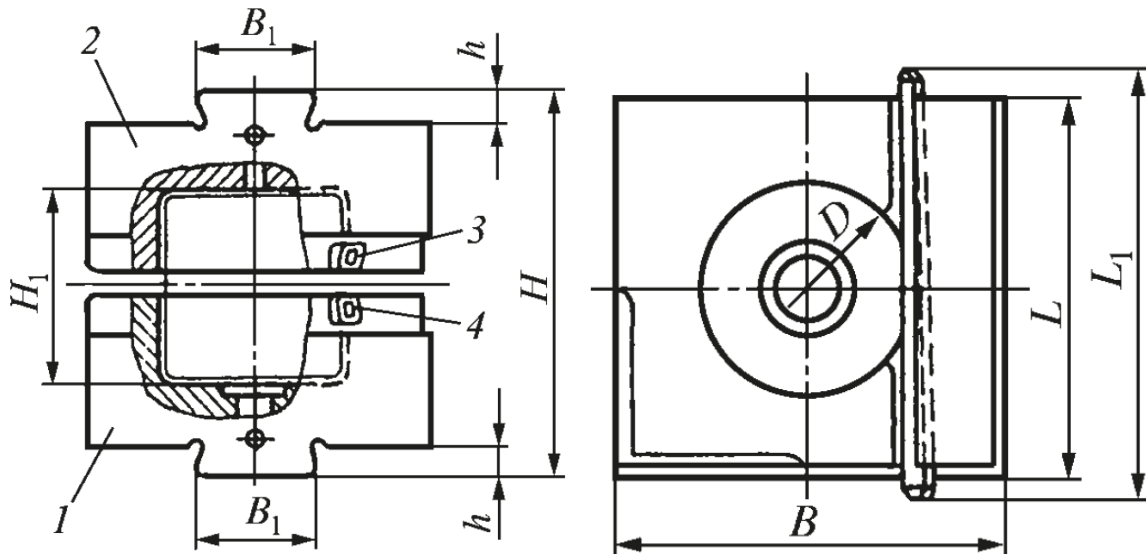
Блоки универсальные молотовых штампов с цилиндрическими вставками [3]:
